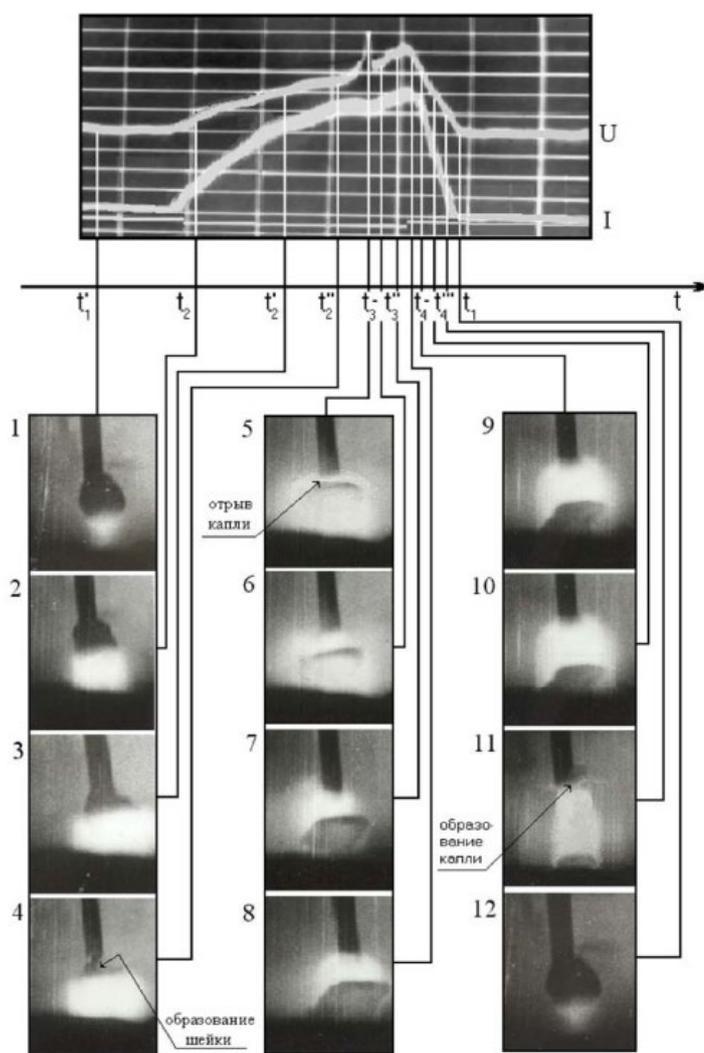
Форма импульса тока и напряжения при сварке импульсной дугой [10]
